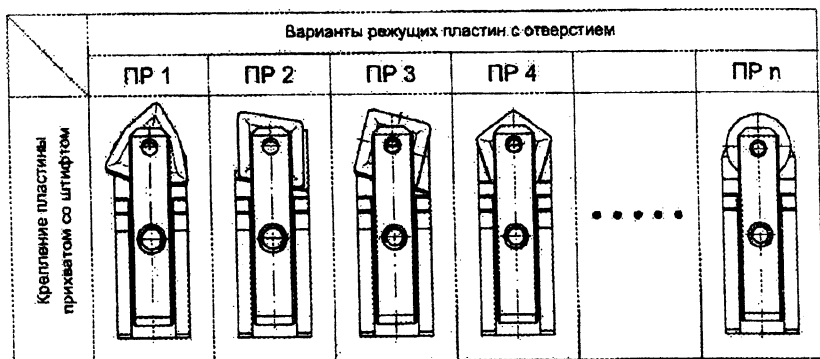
Банк данных резцовых блоков с различными режущими пластинами
